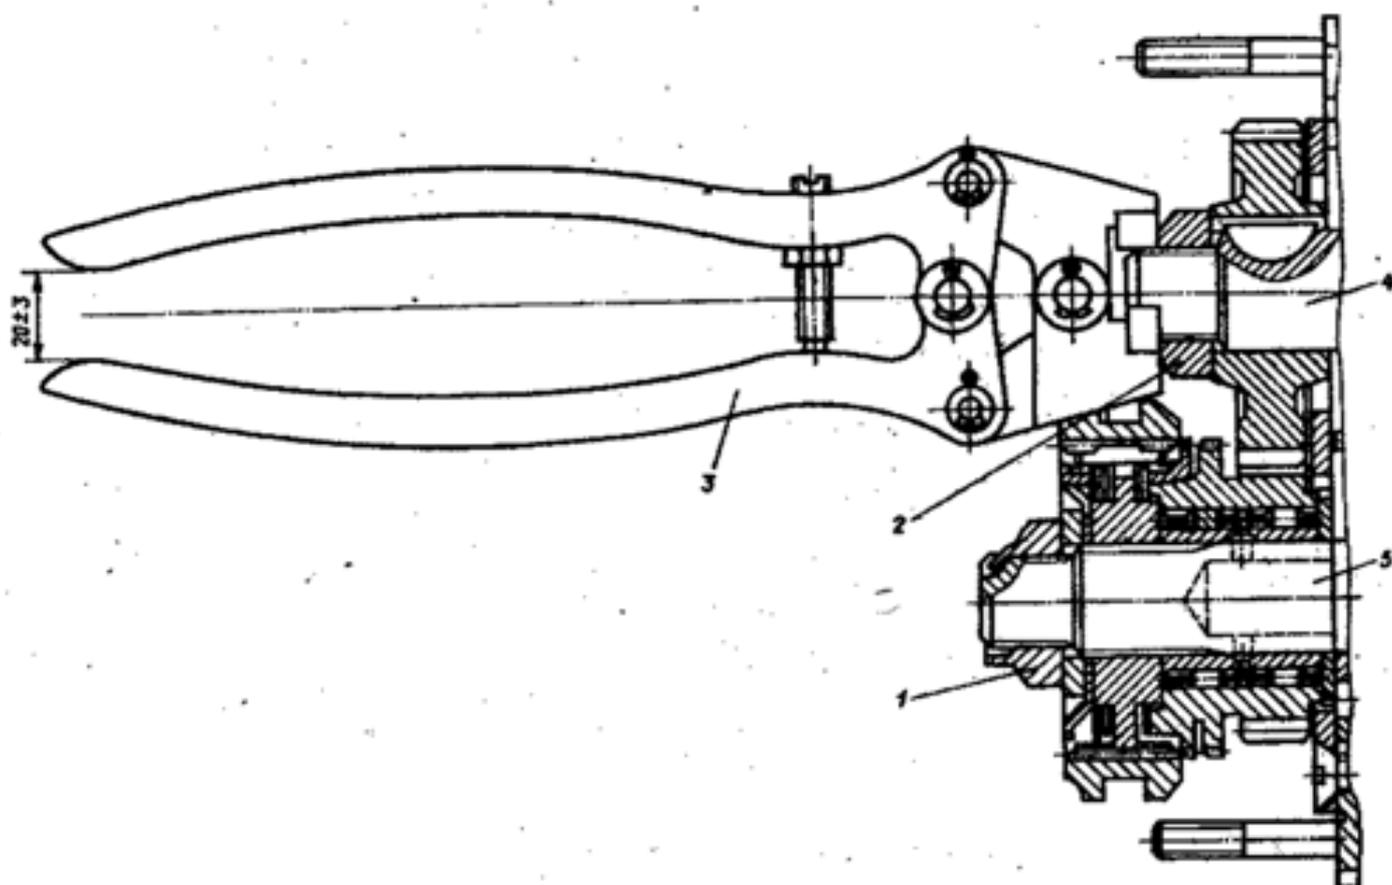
Стопорение гаек ведущего и ведомого валов коробки передач: 1, 2 - гайка ведомого и ведущего валов; 3 - шпильки М9849-403 для стопорения гаек; 4, 5 - ведущий и ведомый валы
